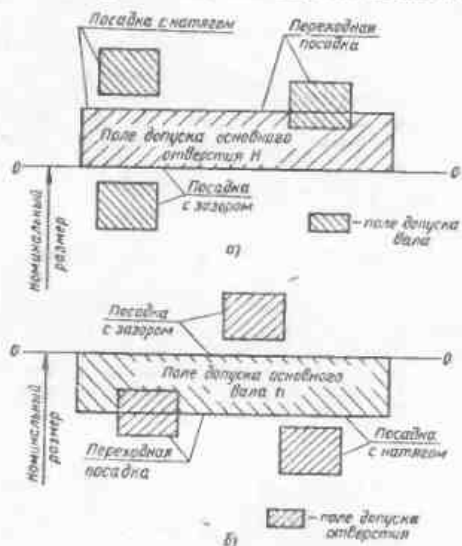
Расположение полей допусков отверстий и валов:
